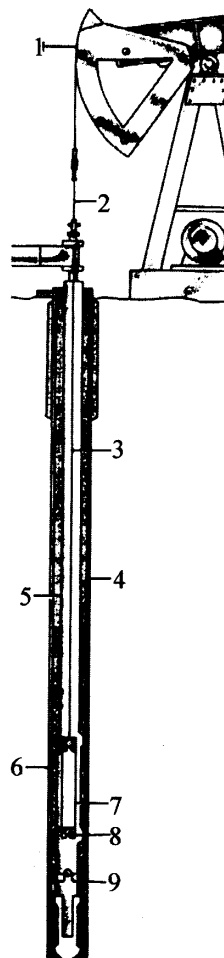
Штанговая насосная установка: 1 – станок-качалка; 2 – полированный шток; 3 – колонна штанг; 4 – обсадная колонна; 5 – насосно-компрессорные трубы; 6 – цилиндр; 7 – плунжер насоса; 8 – нагнетательный клапан; 9 – всасывающий клапан
